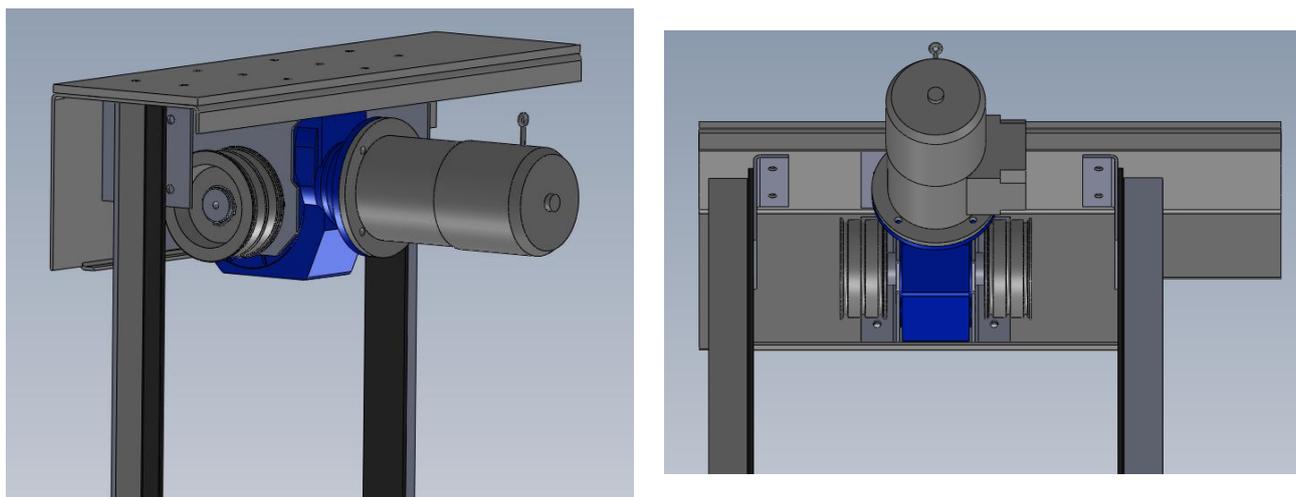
Disegno 3D del particolare 'Trave di sostegno della macchina'
